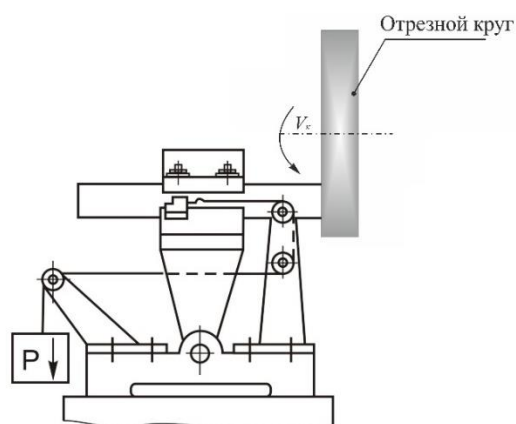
Общий вид приспособления для исследования режущей способности боковых поверхностей отрезных кругов
